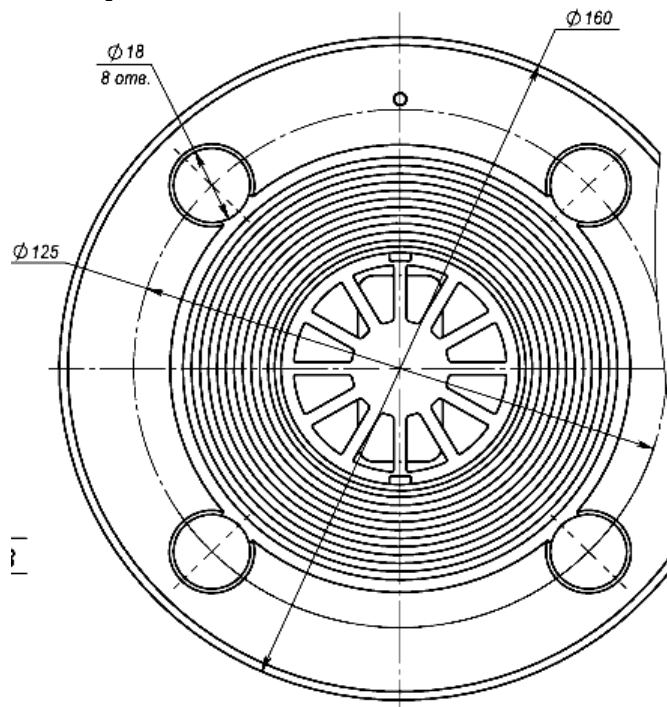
Фрагмент чертежа счётчика с габаритными и установочными размерами
